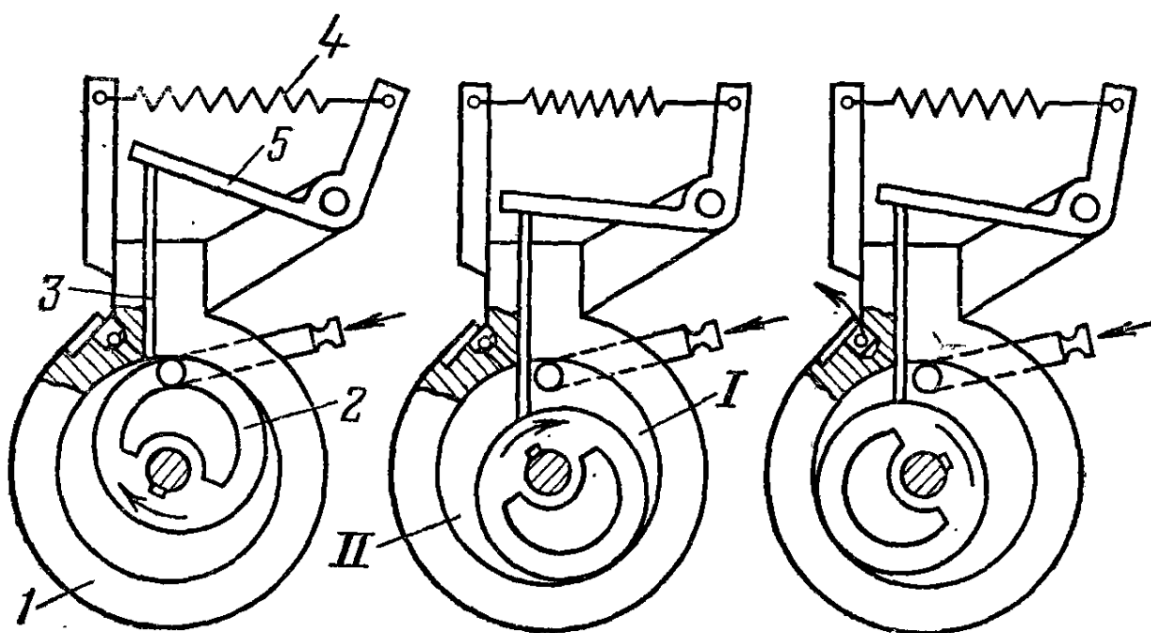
Принцип действия пластинчато-статорного насоса. 1 – цилиндрический корпус; 2 – эксцентрический ротор; 3 – пластина; 4 – пружина; 5 – рычаг нажимного механизма; I – полость всасывания; II – полость сжатия [5, с. 95]
